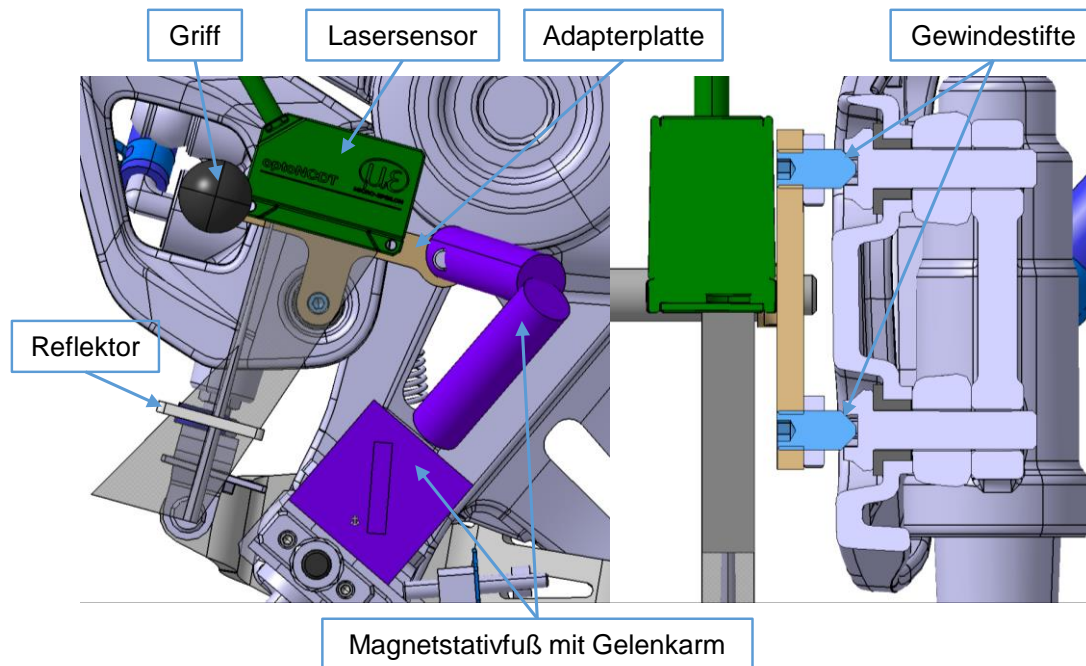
Modul MH0 – Referenzwegmessung am Hauptbremszylinder der Hinterradbremse mittels Lasertriangulationssensor (links) und Schnittansicht der Ausrichtung des Lasers über Gewindestifte an der Verschraubung der Hauptbremszylinder (rechts).
